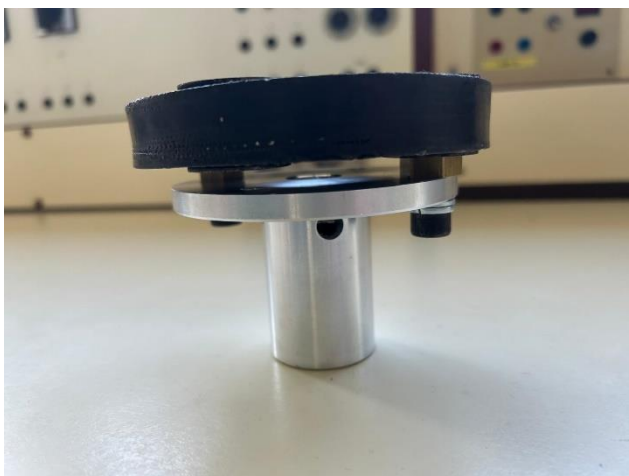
Adapter von unserem Motor auf Wirbelstrombremse
